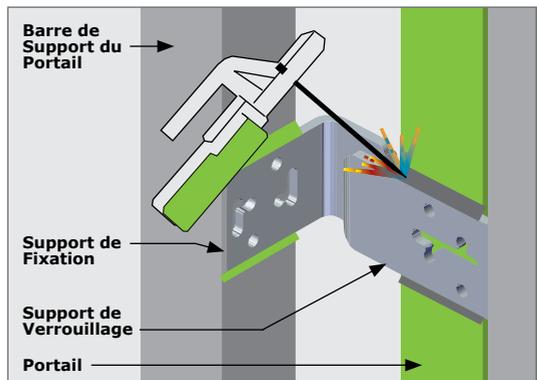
BARRE DE SUPPORT - SOUDÉE
